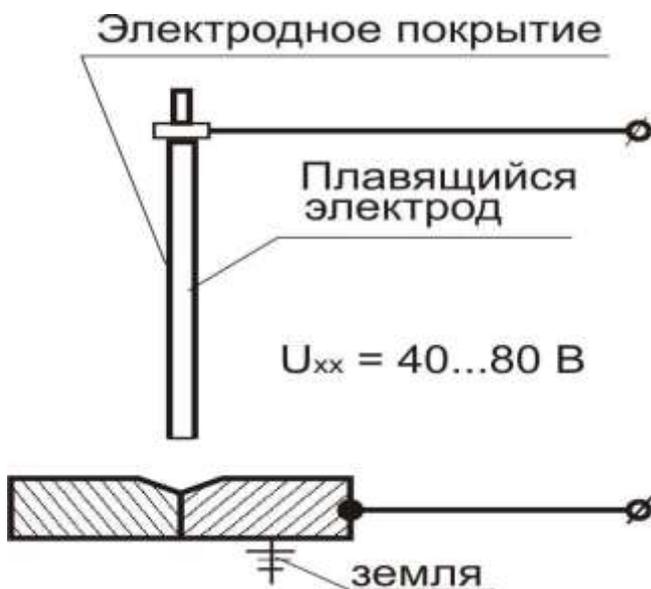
Схема ручной дуговой сварки плавящимся электродом
